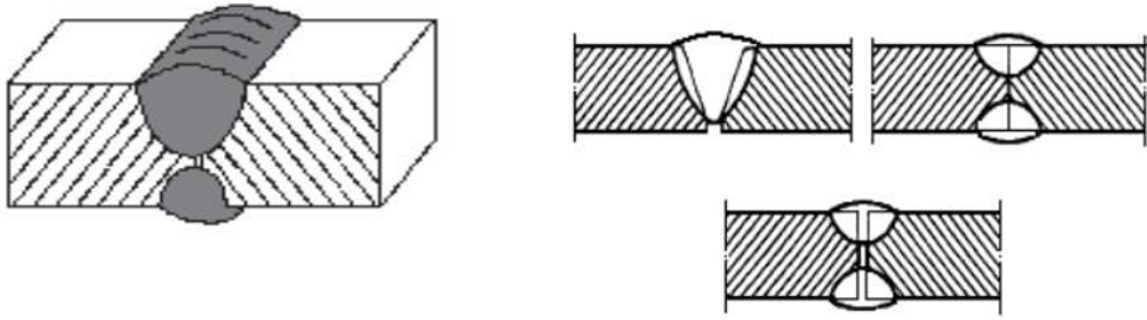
Эскиз дефекта сварного шва
